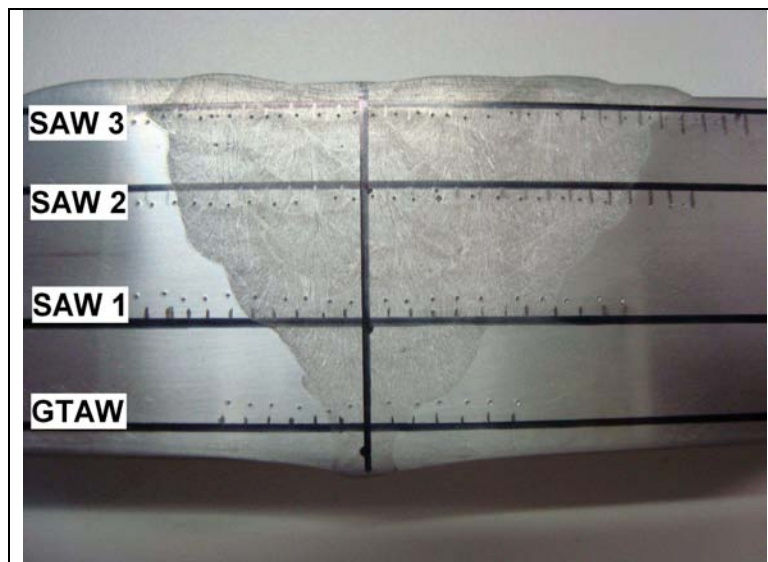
Perfil de durezas levantado ao longo da seção transversal em diversas regiões da junta.
